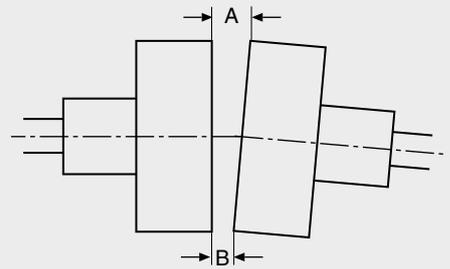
Abgewinkelte Ausrichtung. A-B = max. 0.05 mm.
